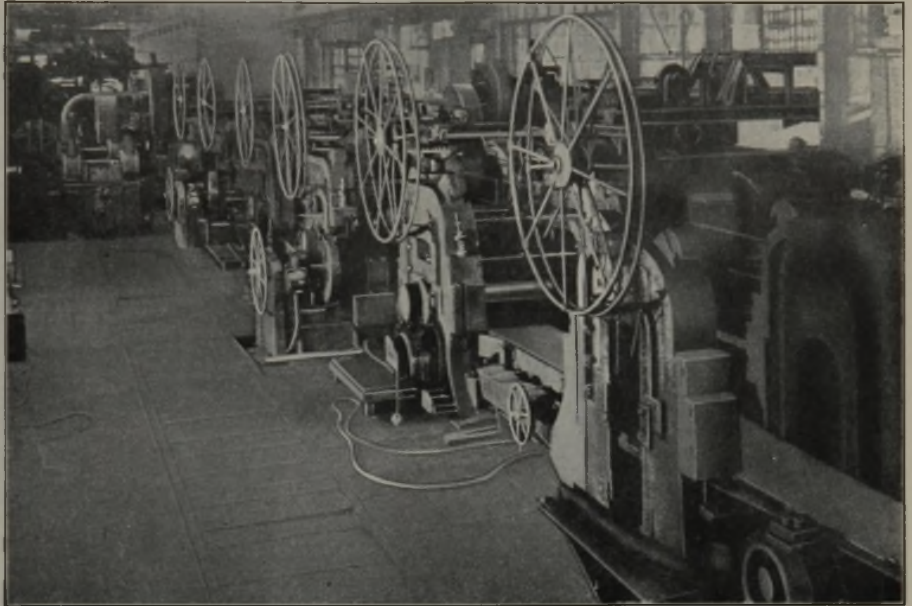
Langblechwalzwerk; im Hintergrund Brammengerüst.
